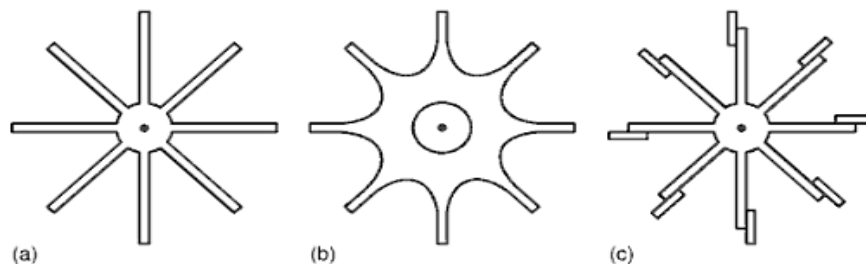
Tipos de rotor de válvula rotativa. a) Rotor de bolsillo profundo, b) Rotor de baja profundidad, c) Rotor con puntas
